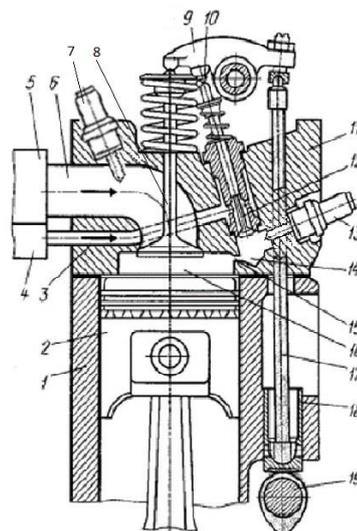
Газодизельный двигатель с форкамерным зажиганием
